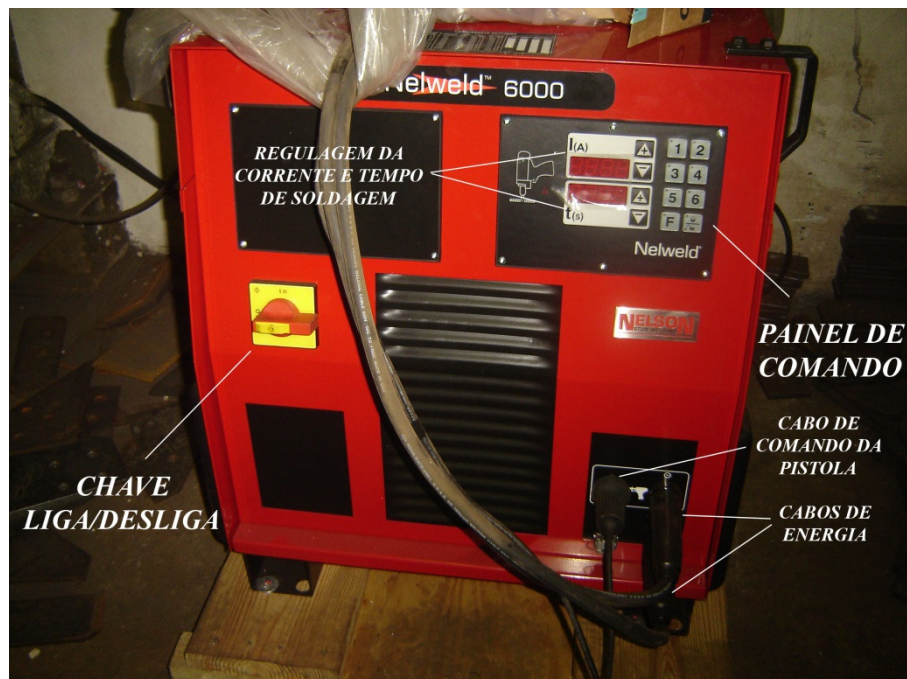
Fonte de soldagem de pinos por eletrofusão Nelweld 6000
